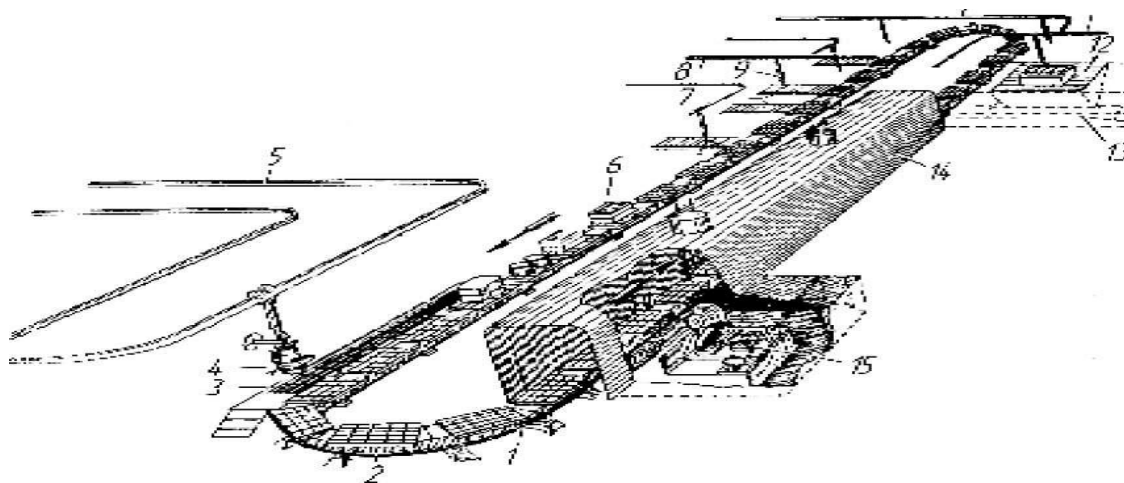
Литейный конвейер: 1 - заливочная площадка; 2 - заливочный ковш; 3 - монорельс; 4 - форма; 5 - формовочные машины; 6 - рольганги; 7 - пневматический подъемник; 8 - выбивная решетка; 9 - транспортер; 10 - охлаждающая камера; 11 - привод; 12 - тележки; 13 – рельсы
